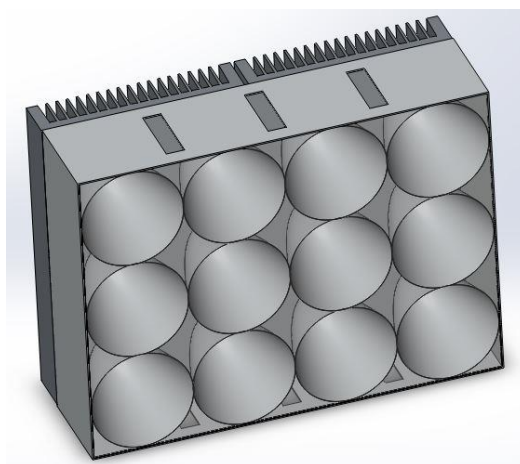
3D модель прожектора с щелями в корпусе
